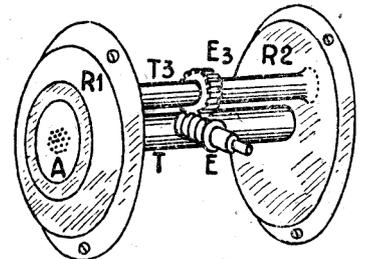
Ensemble des grilles et des éléments oscillants d'un klystron : A, grille d'entrée; E, E₃, engrenages commandant la rotation du tube T₃; R₁, R₂, rhumbatrons d'entrée et de sortie.
